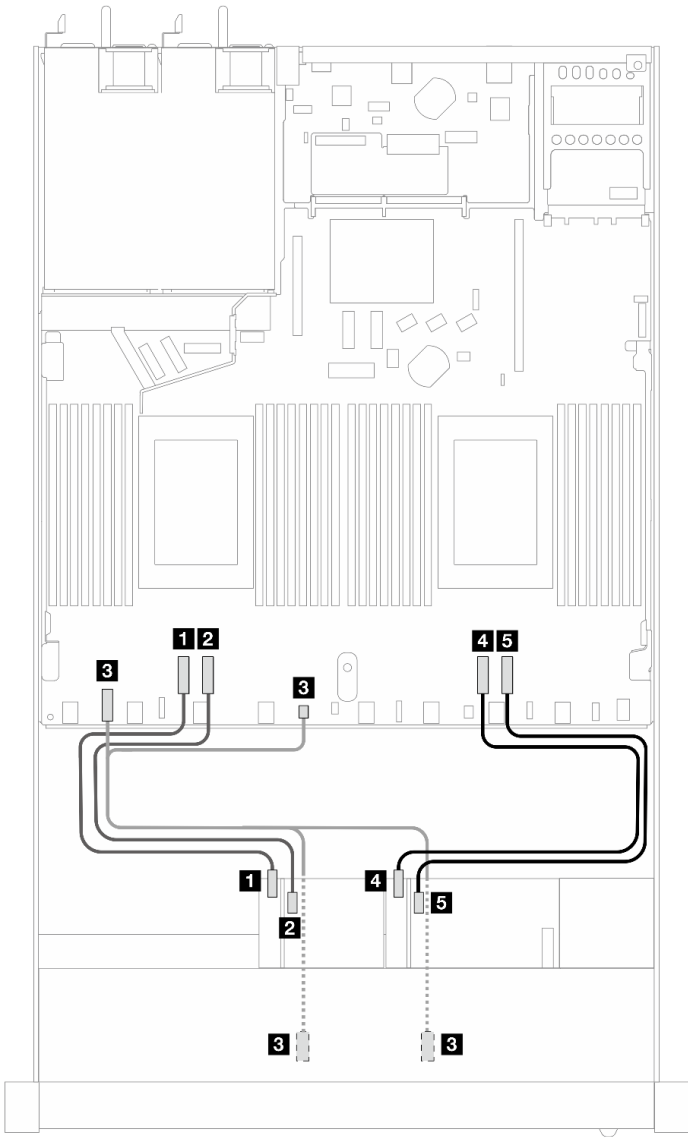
Roteamento de cabos do conjunto da placa riser frontal
